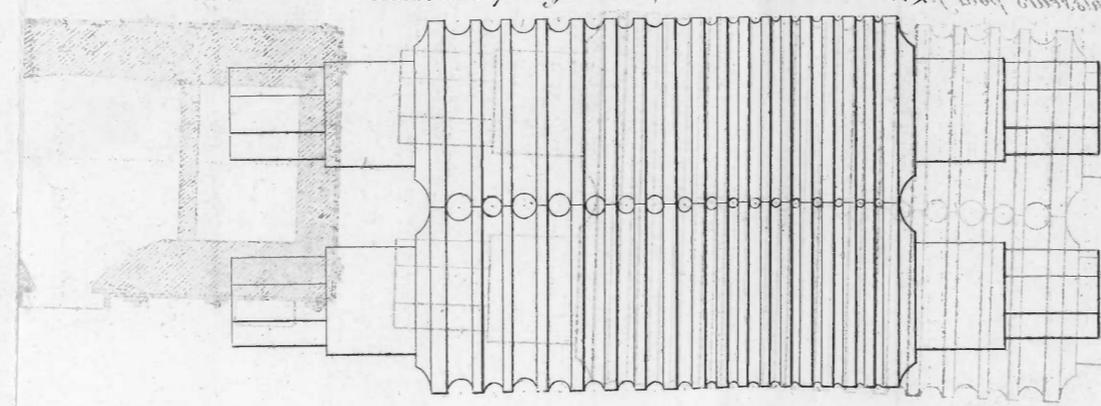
Plan à la hauteur C.D. Fig. 2.
